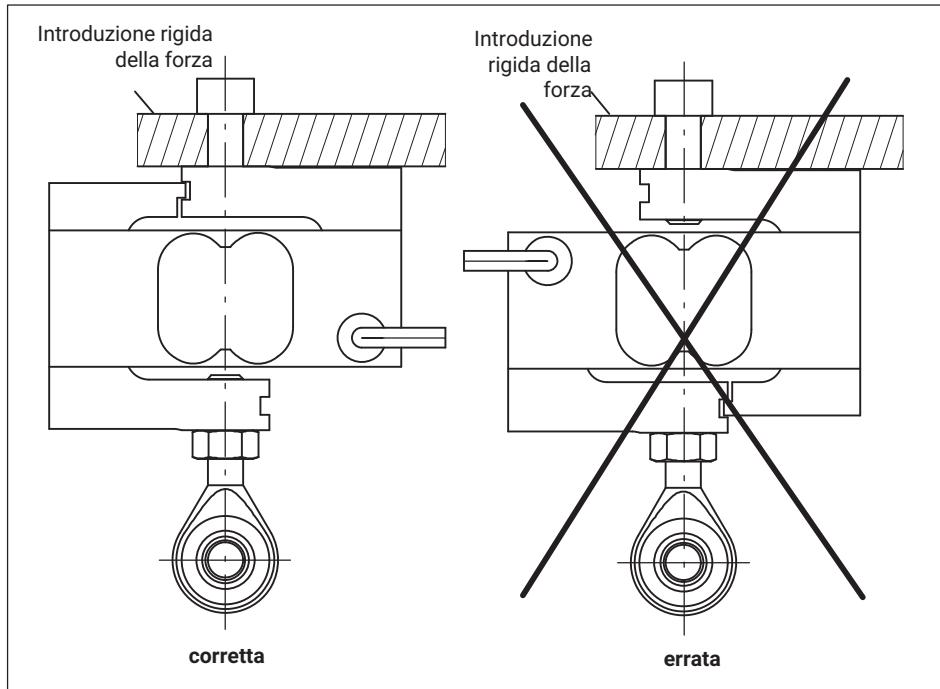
Orientamento del trasduttore durante il montaggio
